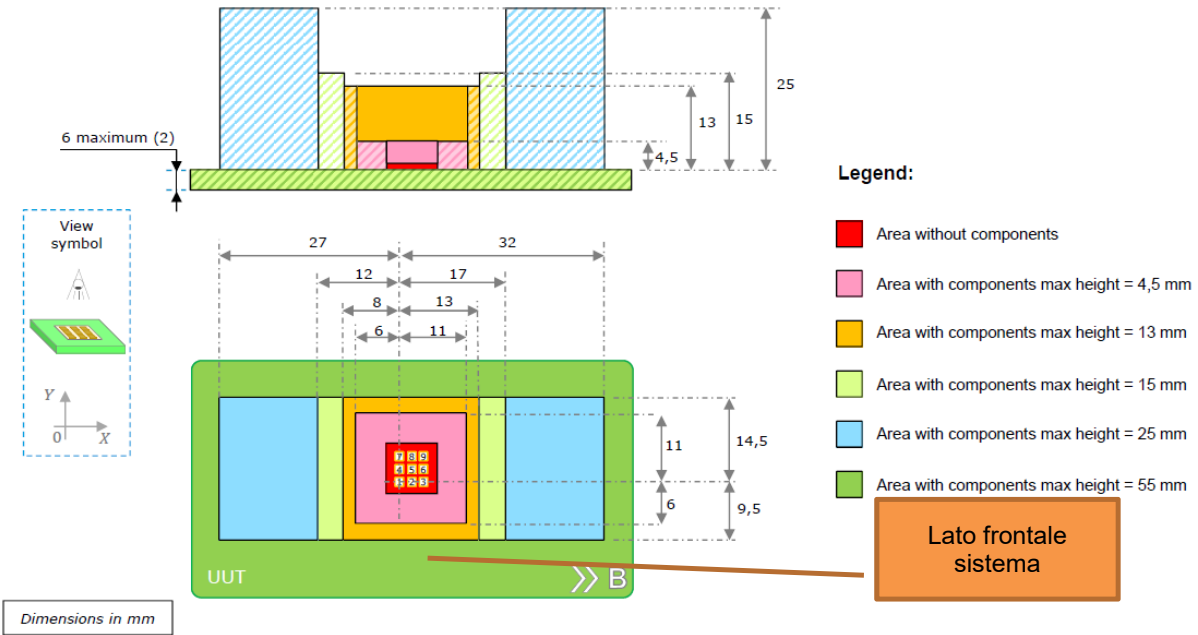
Dimensione della pad e layout lato superiore 1 e 4 MPU [dimensioni in mm]
